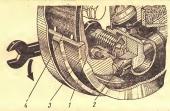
Регулировка зазора между колодками и тормозным барабаном автомобили ГАЗ-69: 1— регулировчими винт; 2— разжимной палец; 3— барабан; 4— накладка нолодки.
